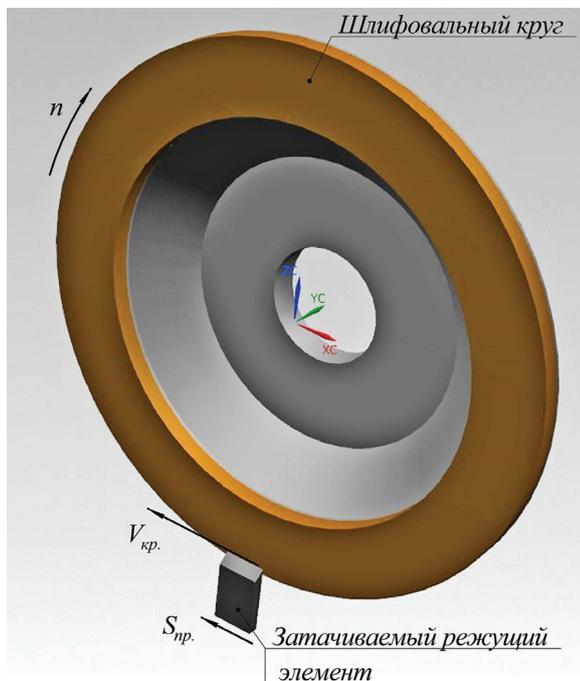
Принципиальная схема алмазного затачивания твердосплавного режущего элемента
